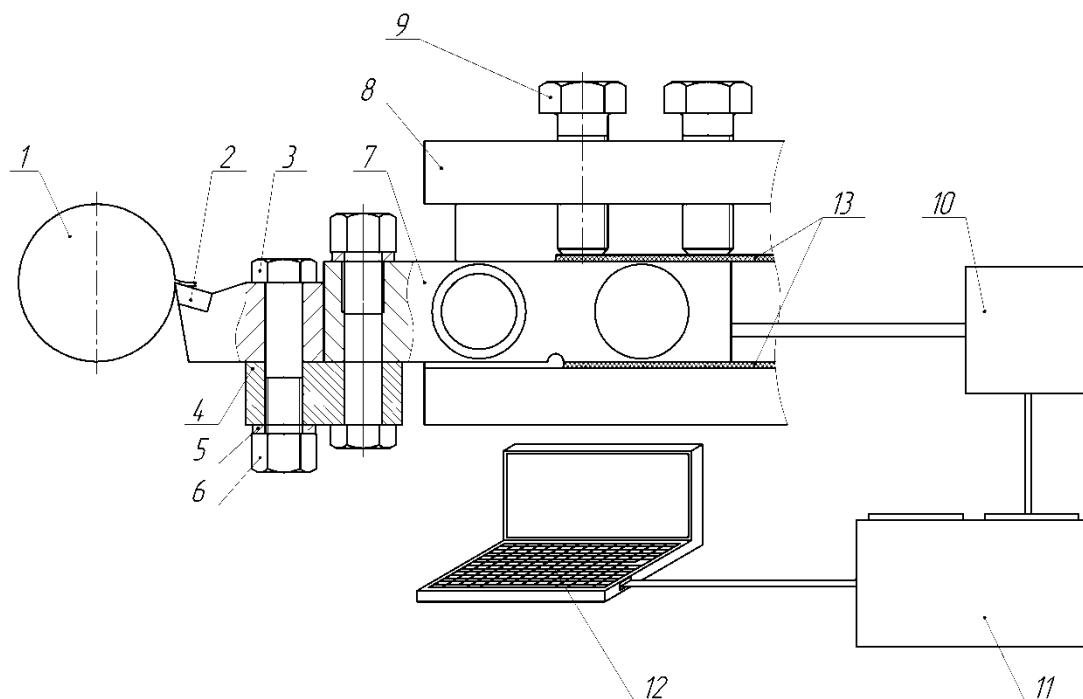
Схема установки для измерения силы резания: 1 – обрабатываемая деталь; 2 – резец; 3 – болт М12; 4 – трубка; 5 – шайба; 6 – гайка М12; 7 – балочный тензодатчик SBA; 8 – резцедержатель; 9 – винты резцедержателя; 10 – усилитель сигнала датчика; 11 – плата сбора данных NI USB 6210; 12 – персональный компьютер
